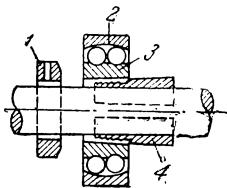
Монтажный стакан для одновременной запрессовки шарикоподшипника на вал и корпус.
